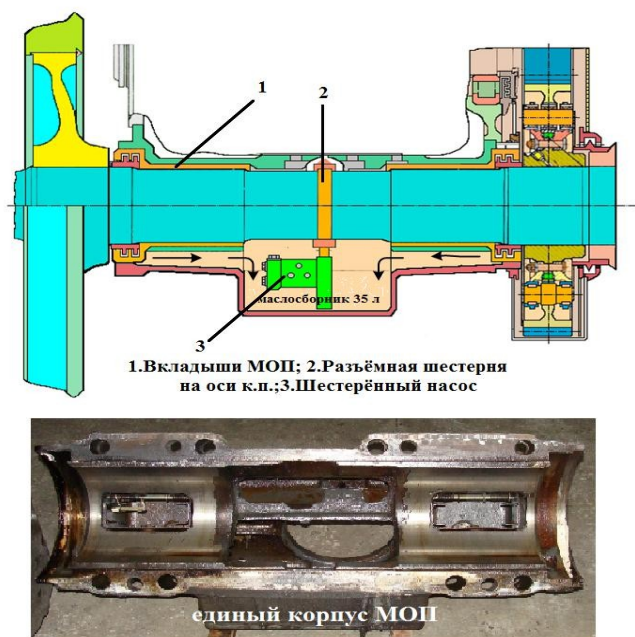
Единый осевой подшипник двигателя ЭД-118Б
